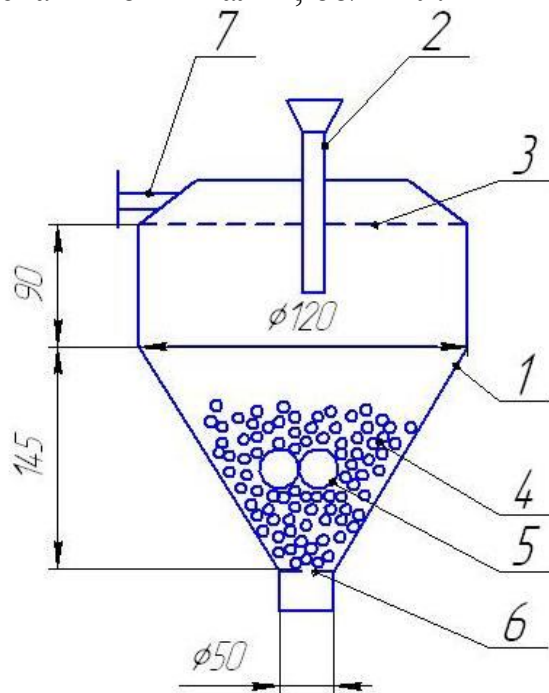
Сушарка з інертним носієм: 1 - циліндро-конічний корпус; 2 - відбійна решітка; 3 - загрузочна воронка; 4 - вхідний патрубок повітря; 5 -
